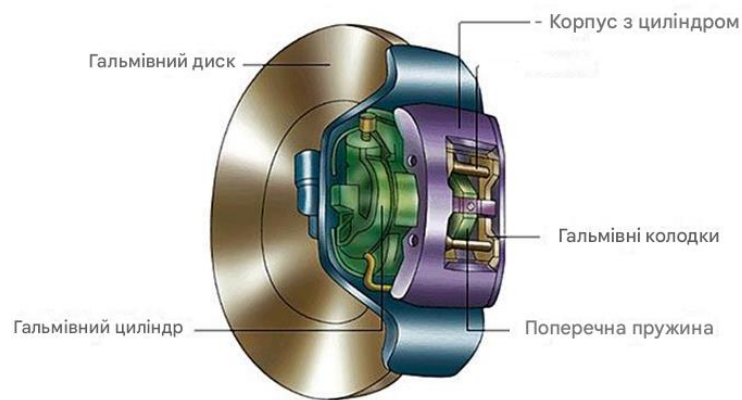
Конструкція дискового гальмівного механізму [2]
